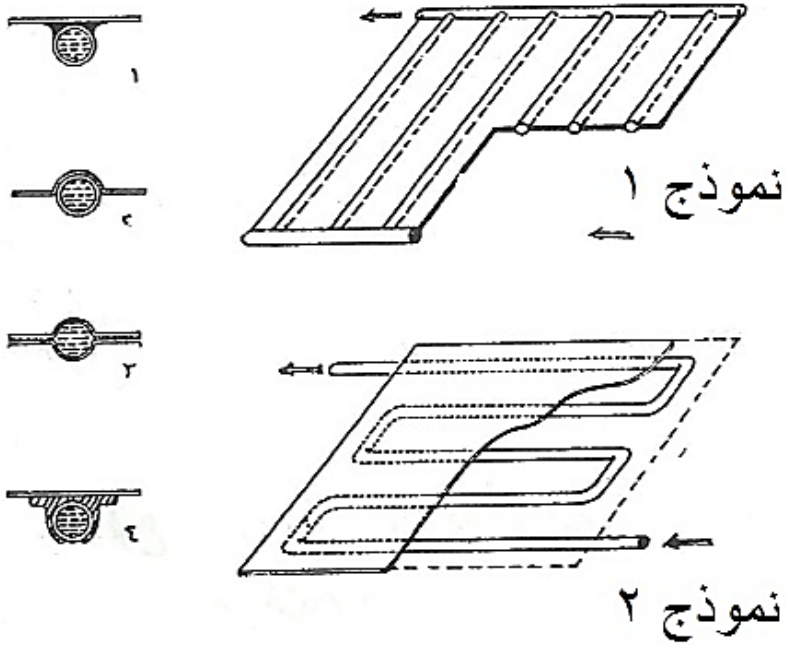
مقطع عرضي في مجمع شمسي مسطح
